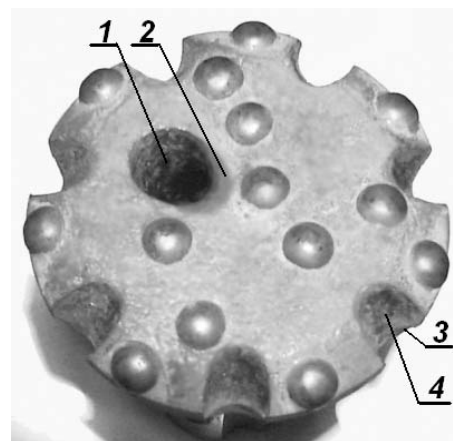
Экспериментальная штыревая коронка: 1 – продувочный канал; 2 – торцевой паз, связанный с продувочным каналом; 3 – боковой паз; 4 – торцевой паз, связанный с боковым пазом
